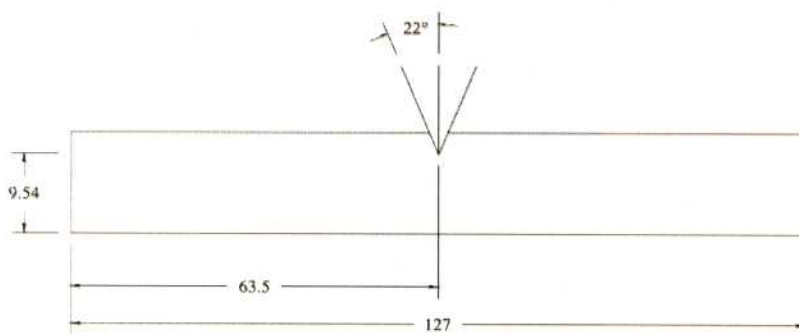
Dimensiones de la probeta y la entalla (medidas en mm).
